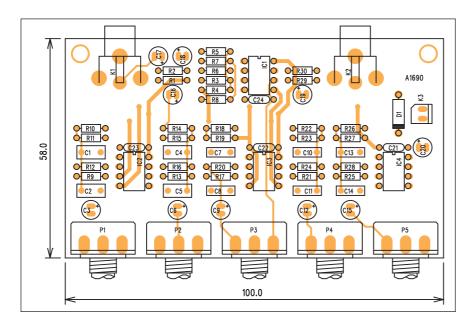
Obrazec desky spojů crossoveru (strana BOTTOM)
